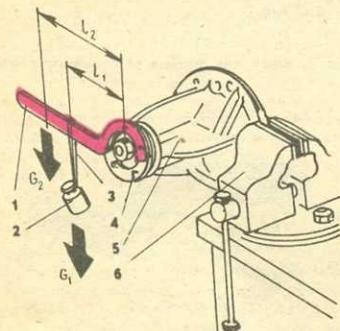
Проверка предварительного натяга в подшипниках ведущей шестерни при помощи ключа: 1 — ключ для фланца ведущей шестерни; 2 — груз [гири]; 3 — нить; 4 — фланец ведущей шестерни; 5 — картер редуктора; 6 — тиски.
